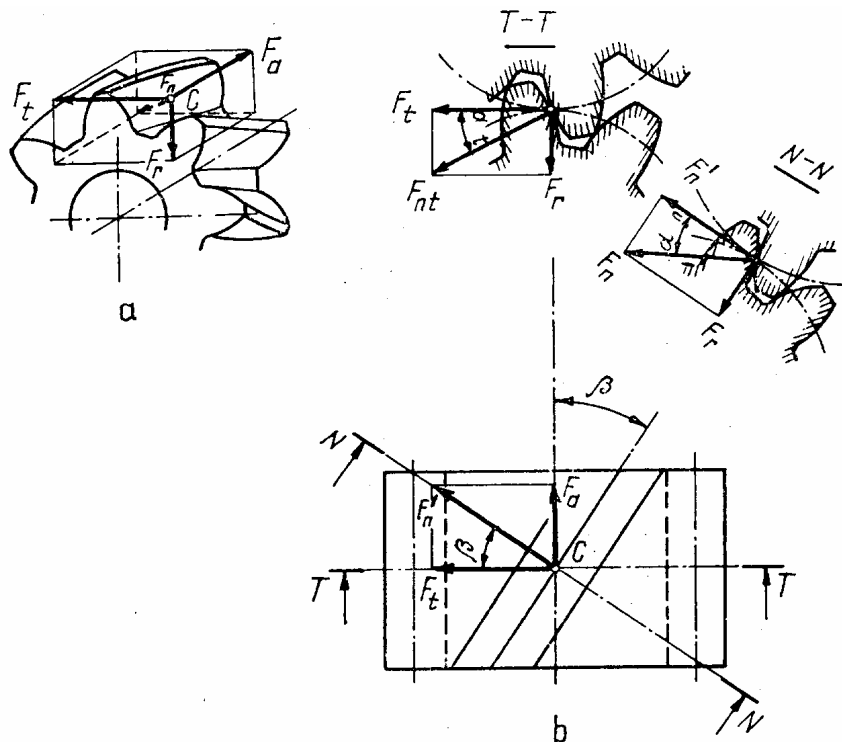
Forces dans un engrenage cylindrique hélicoïdal.
